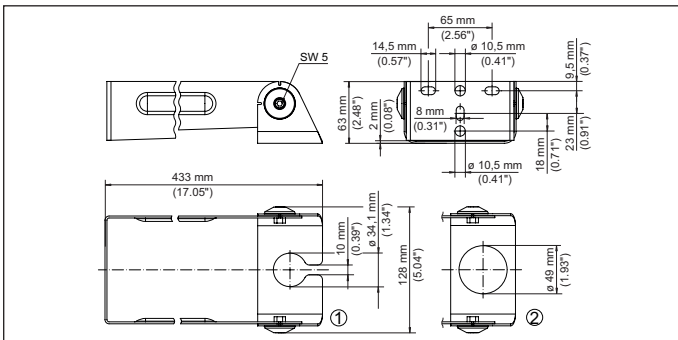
arco de montagem para montagem na parede - suporte 200 mm
